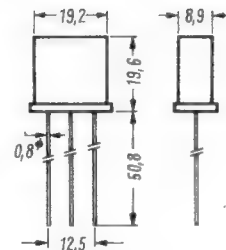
Gehäuseabmessungen des kompletten Quarzoszillators QO 19
